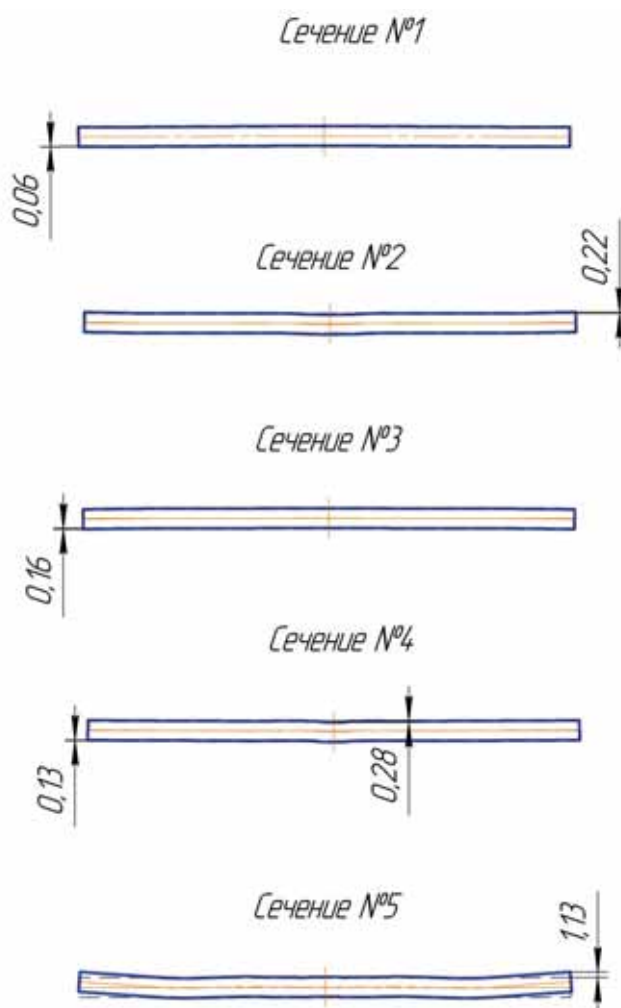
Сечения для каждой из пяти полос свариваемых пластин, отражающих характер коробления сварной конструкции
